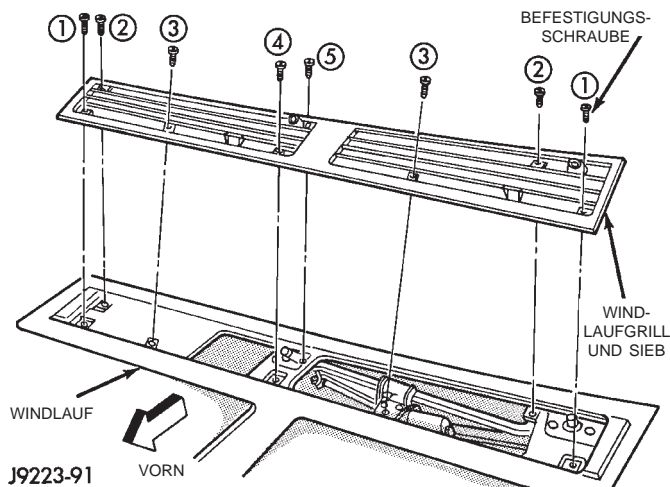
Anzugsfolge der Schrauben am Windlaufgrill
